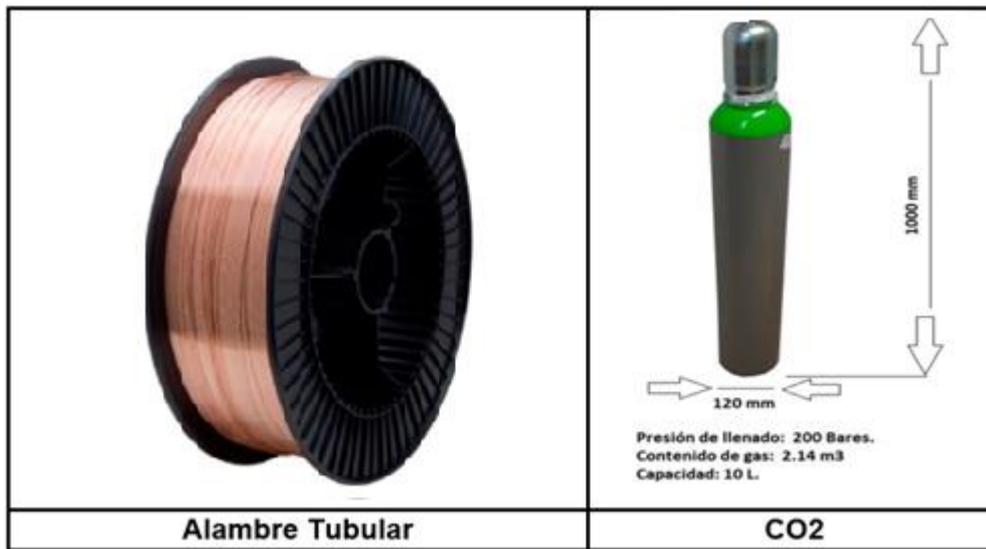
Alambre y gas utilizado para el proceso de soldadura.
